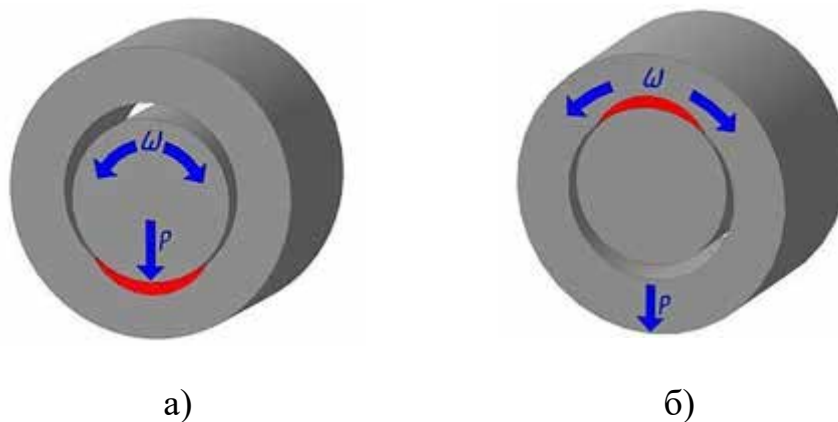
Контактна взаємодія деталей рухомих гладких циліндричних з'єднань: а) – опорний отвір та рухомий вал; б) – опорний вал і елемент з отвором, що спирається на нього
